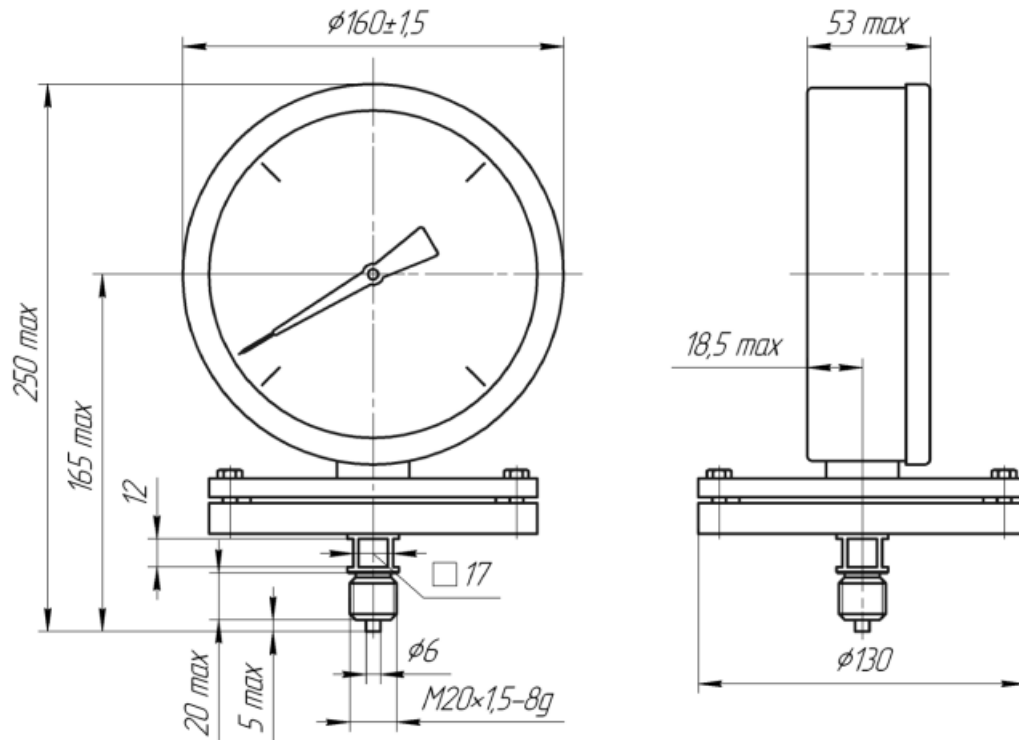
Габаритные и присоединительные размеры приборов исполнения II
